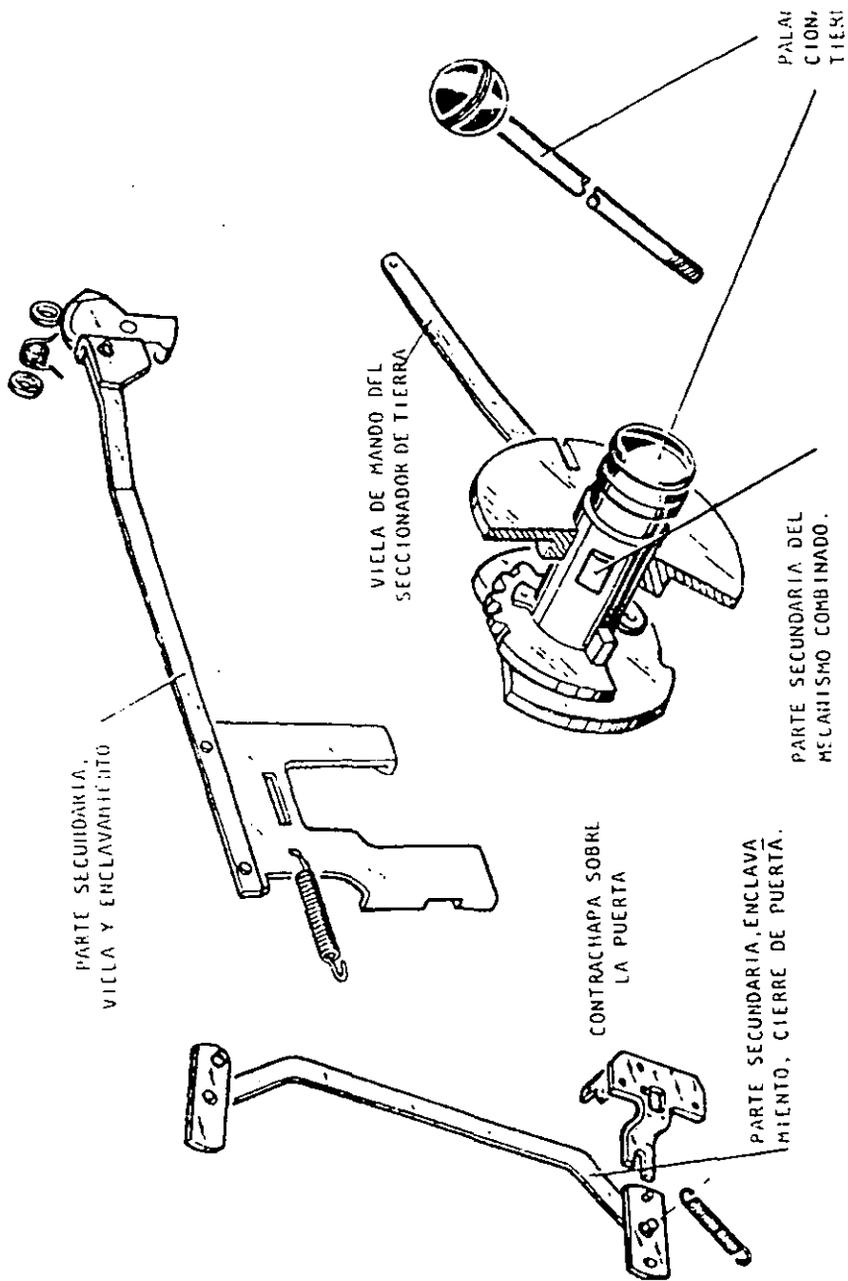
Mecanismos de Maniobras y Enclavamientos del Seccionador de Puesta a Tierra, Interruptor RT6S-400 A. (Sección Dos) y Seccionador SL-400 (Sección Uno).
